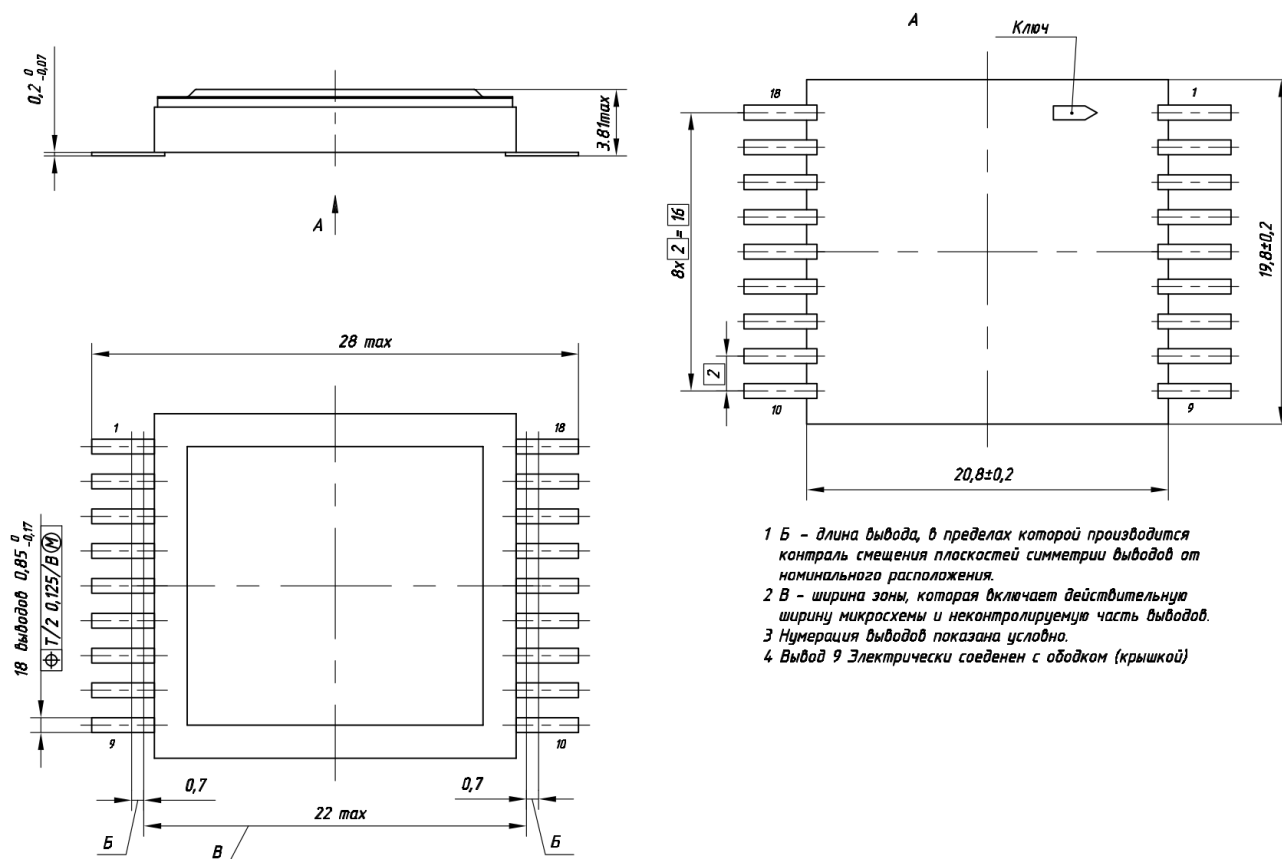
Габаритный чертеж корпуса "Марабу"
